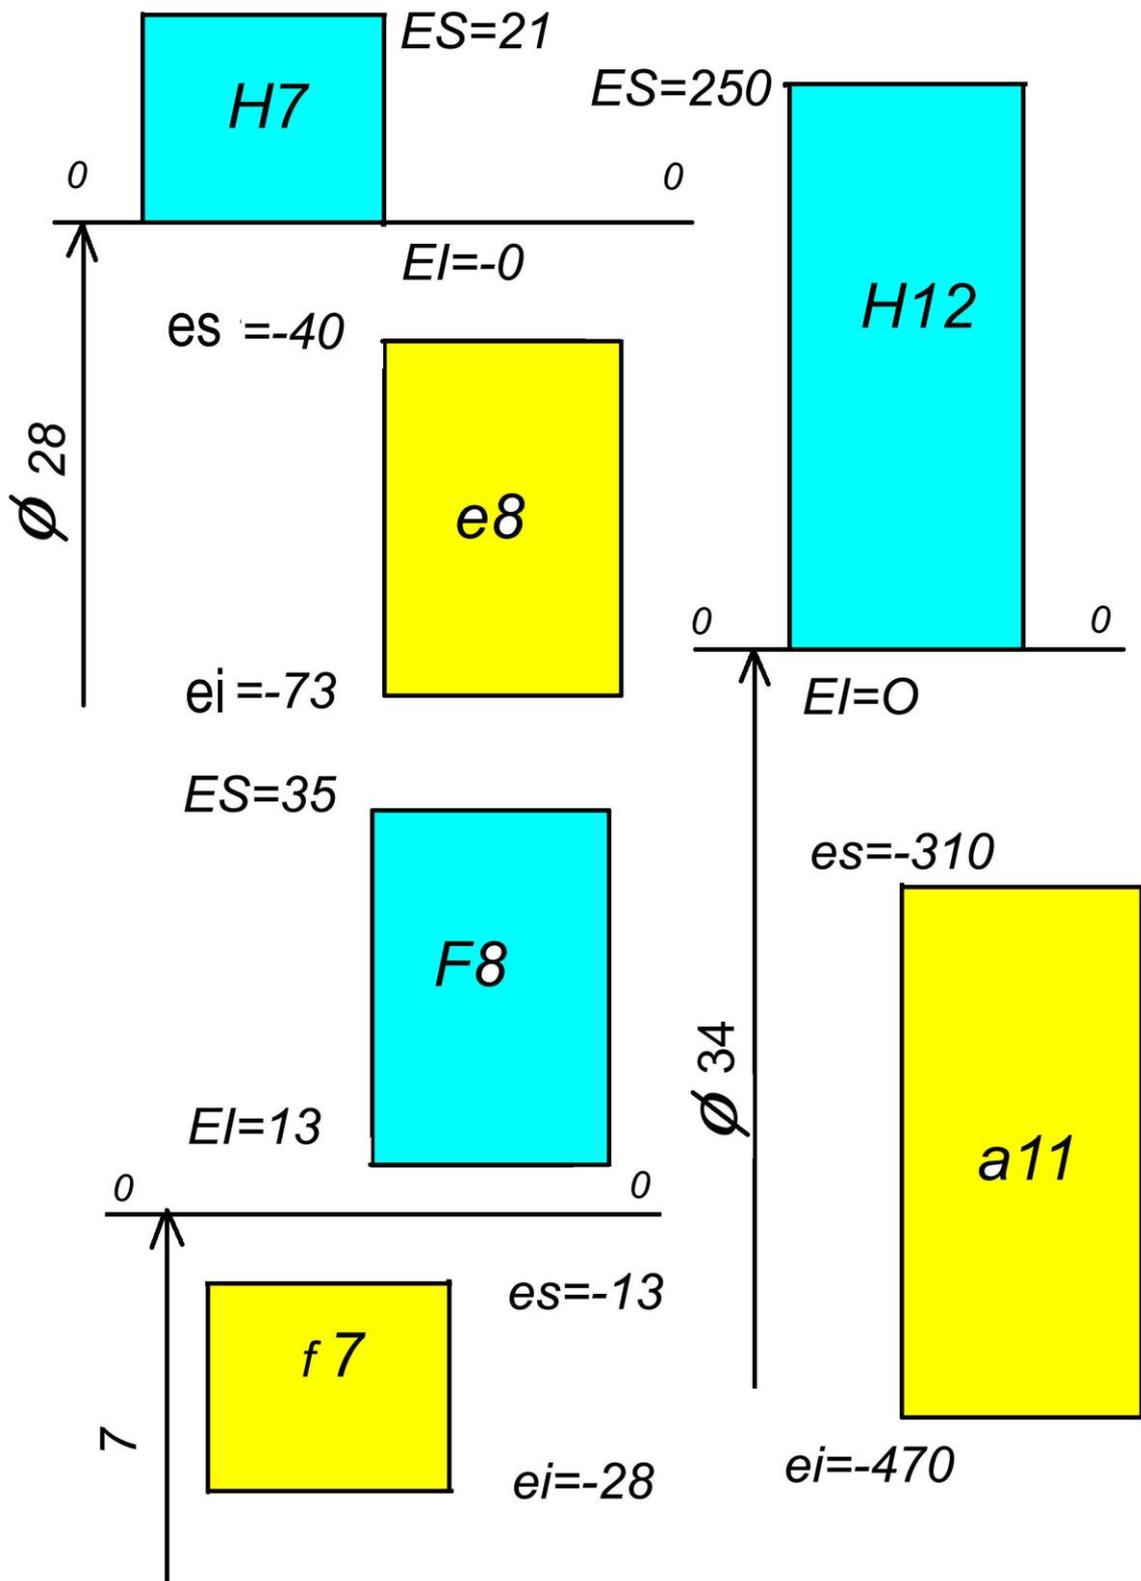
Схема расположения полей допусков для соединения: $d - 6 \times 28H7/e8 \times 34H12/a11 \times 7F8/f7$.
